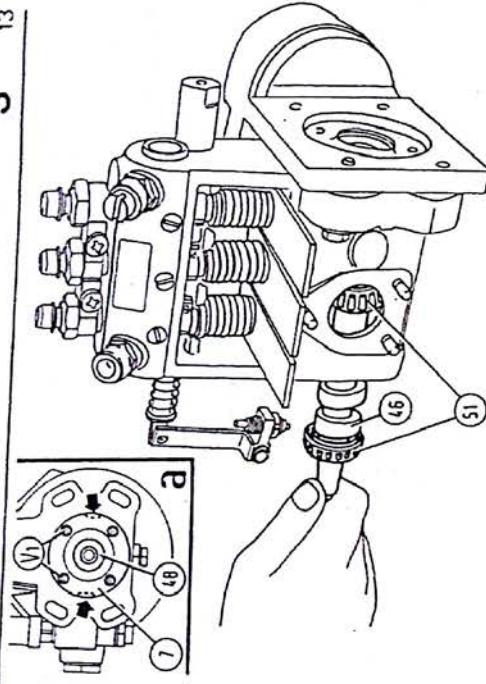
/20 - Dépose (repose) de l'arbre à cames (46)
